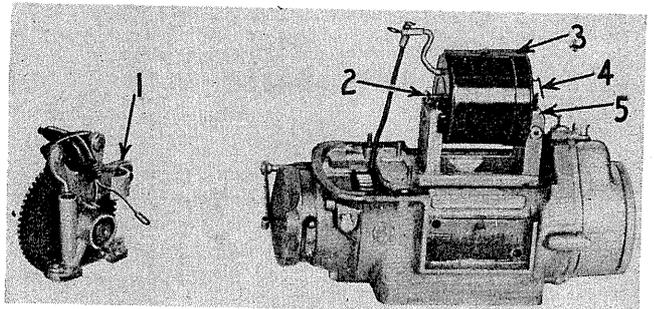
DEMONTAGE DE LA BOBINE.
